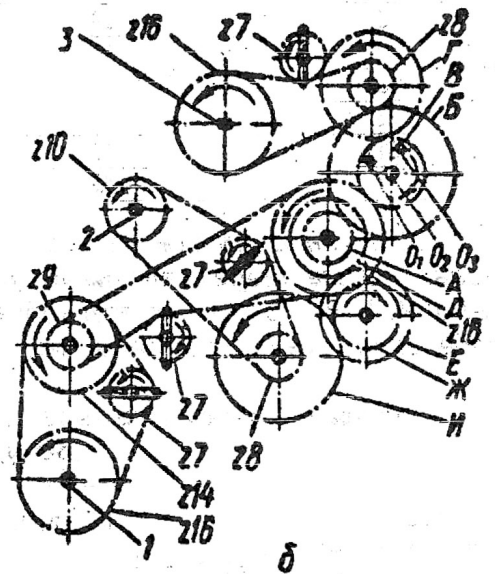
Схема передаточного механизма сеялок типа СЗ-3,6 (СЗ-3,6А) и СЗП-3,6, оборудованных шестеренчатым редуктором вид сбоку:
